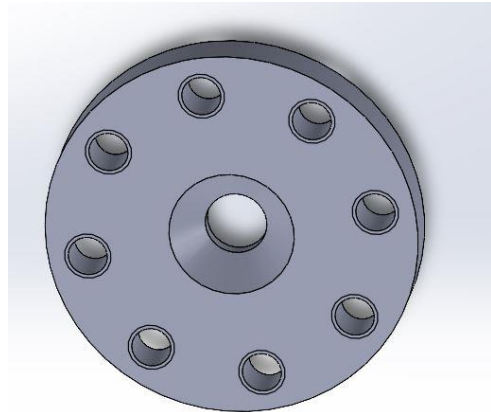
Vista Inferior da flange acoplamento ao sensor
